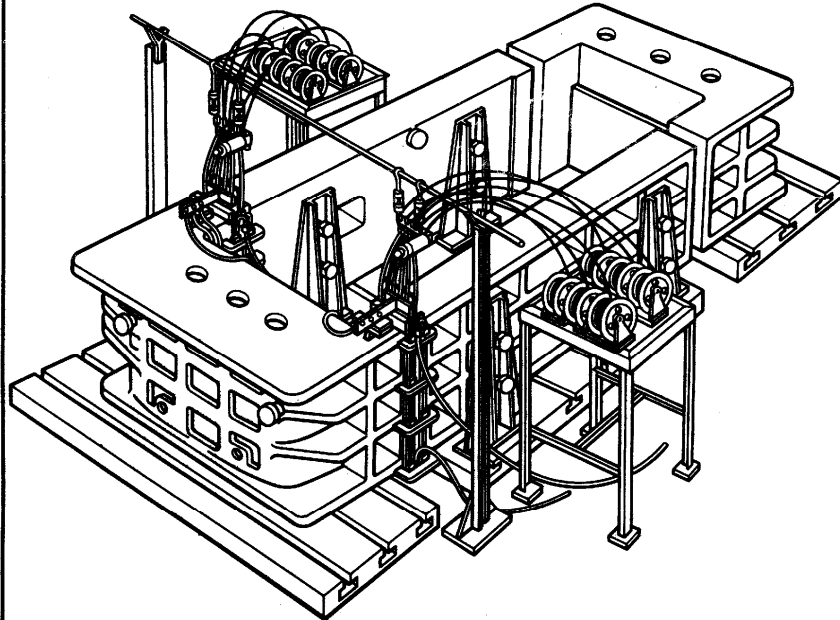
Рама щековой дробилки, собранная под электрошлаковую сварку плавящимся мундштуком
